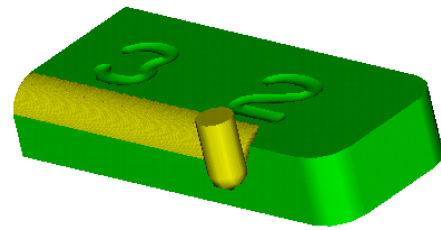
Bearbeitungssimulation eines Stempels für das Ziehwerkzeug mit einem Kugelfräser
